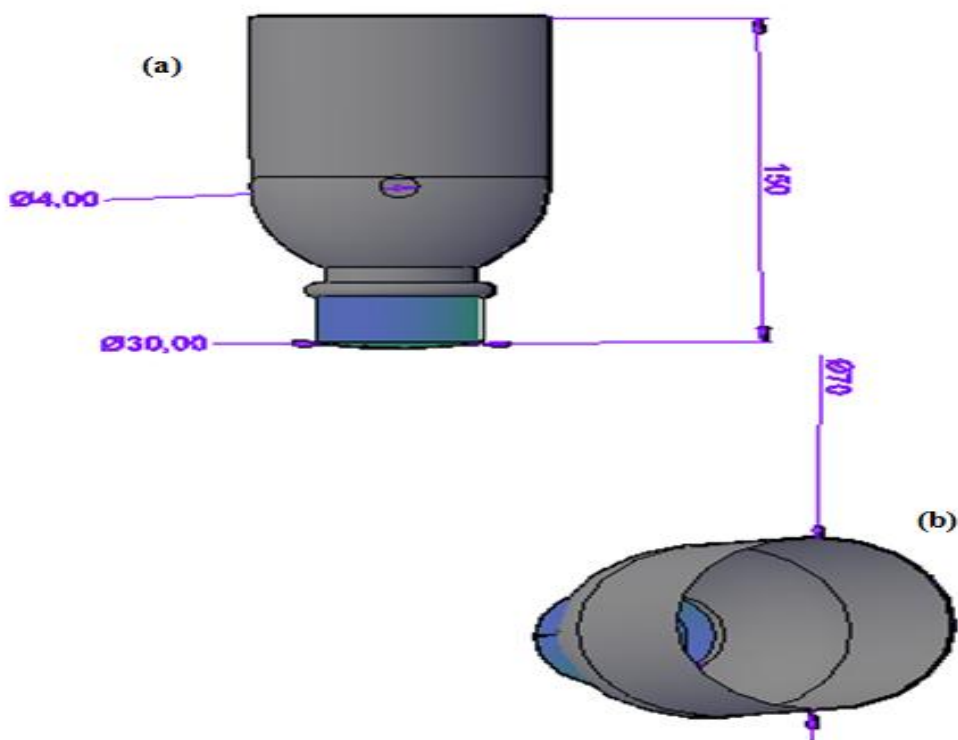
Esquema del tanque. (a) Parte frontal del tanque; (b) Fondo del tanque con un diámetro de 70mm.
